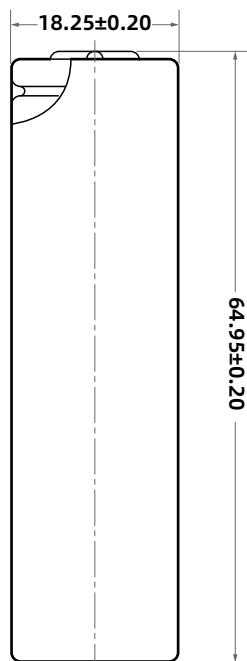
电芯尺寸 / Figure1.Cell dimension. / Рисунок 1. Габариты аккумуляторной ячейки
